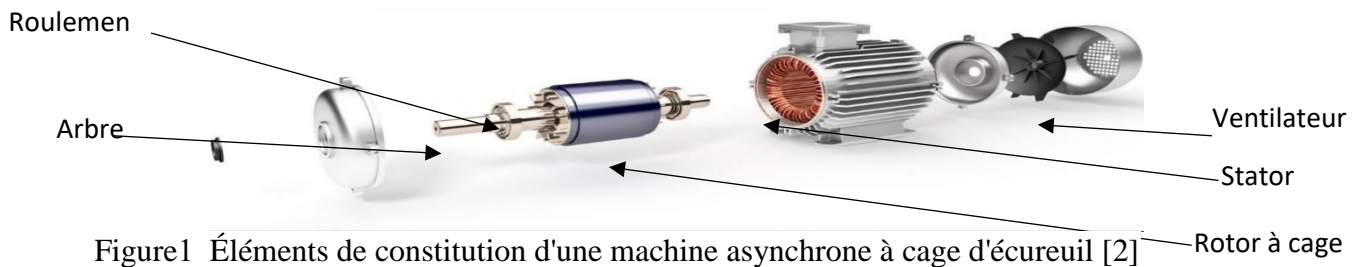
Éléments de constitution d'une machine asynchrone à cage d'écureuil [2]
